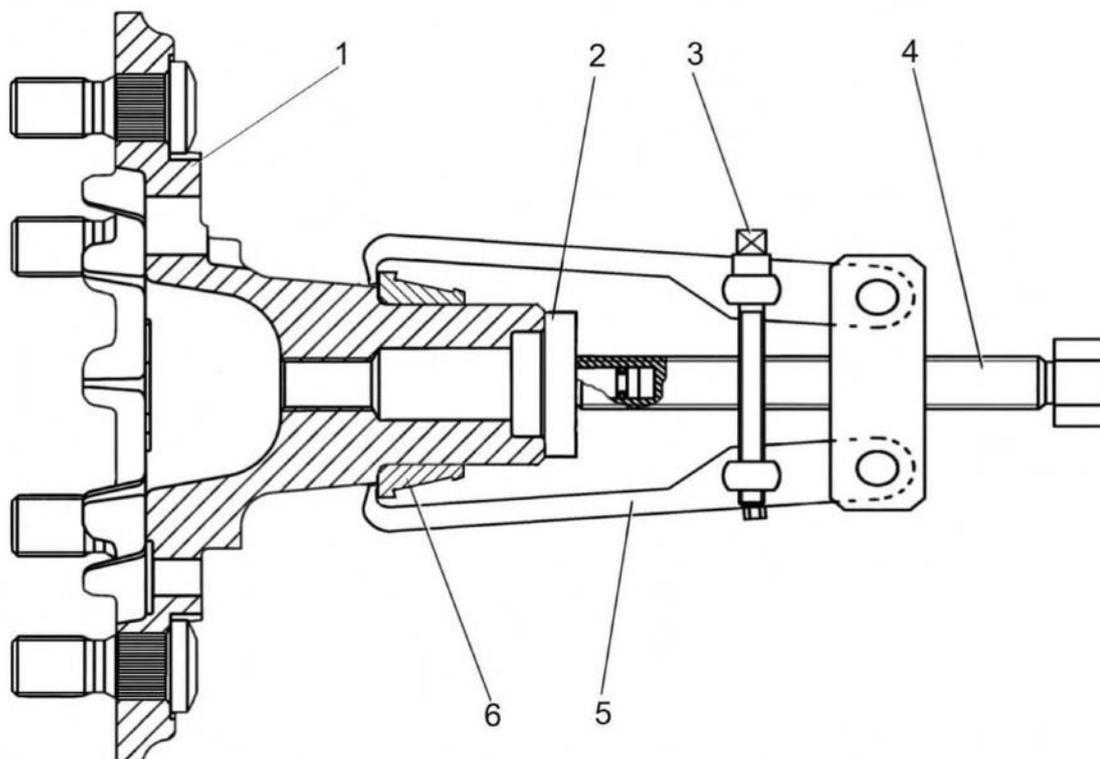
Снятие внутреннего кольца подшипника со ступицы: 1 - ступица; 2 - подпятник; 3 - болт; 4 - винт; 5 - лапка; 6 - внутреннее кольцо подшипника
